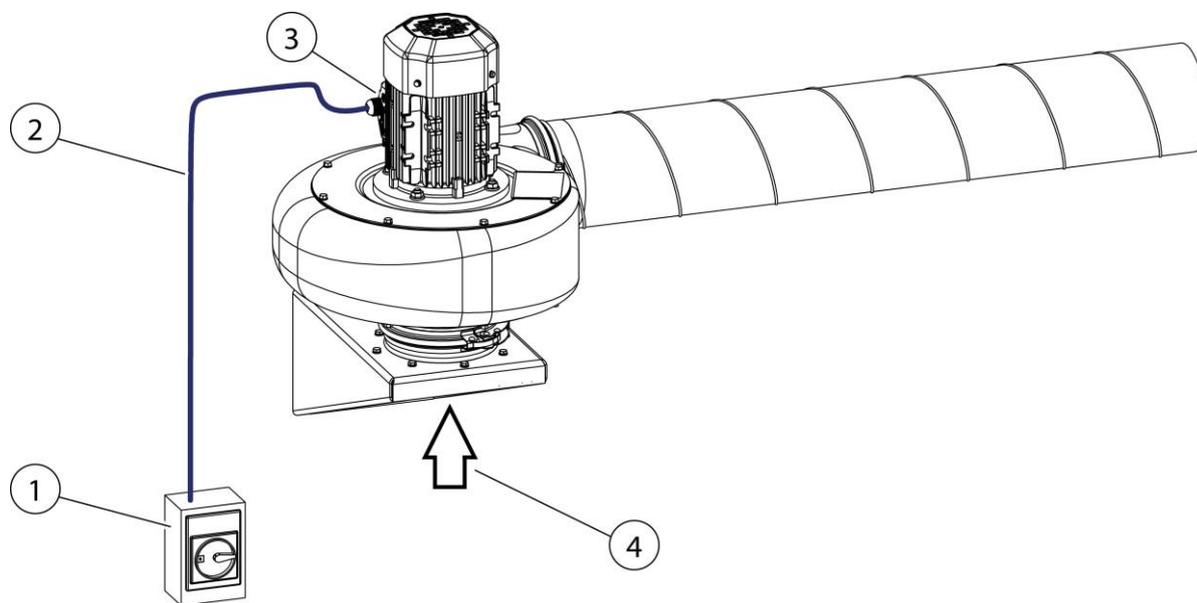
Conexión eléctrica - Ejemplo de montaje
